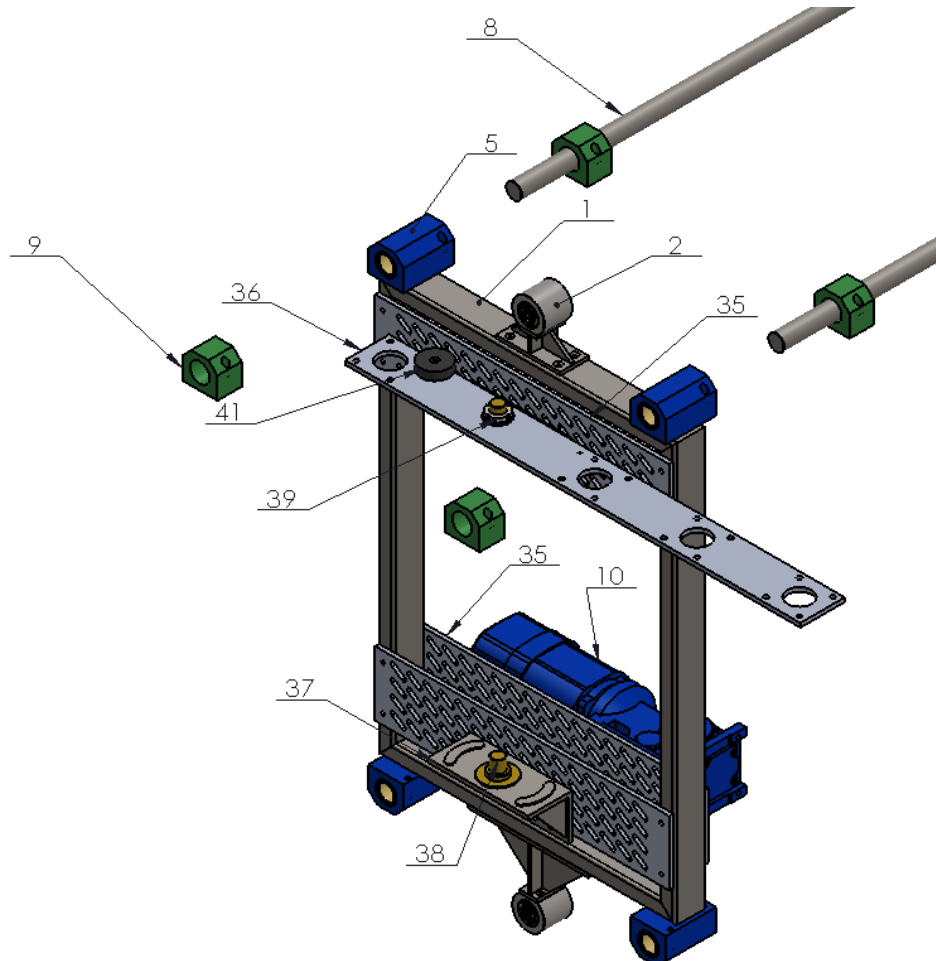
Aro do mecanismo de arraste, representado em vista isométrica explodida e assembled
